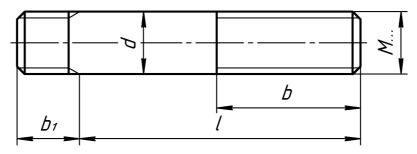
Шпилька по ГОСТ 22032-76...22040—76
